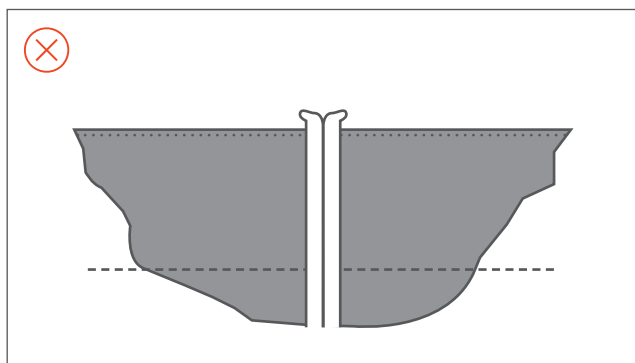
Butt-weld with hardly beads (onacceptable)
